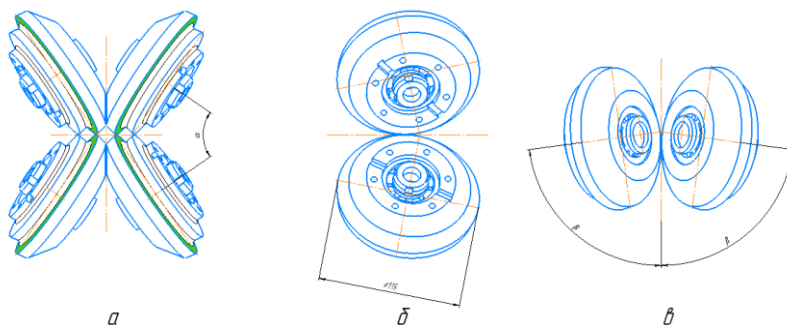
Загальний вид розташування прокатних валків для триниткової прокатки
